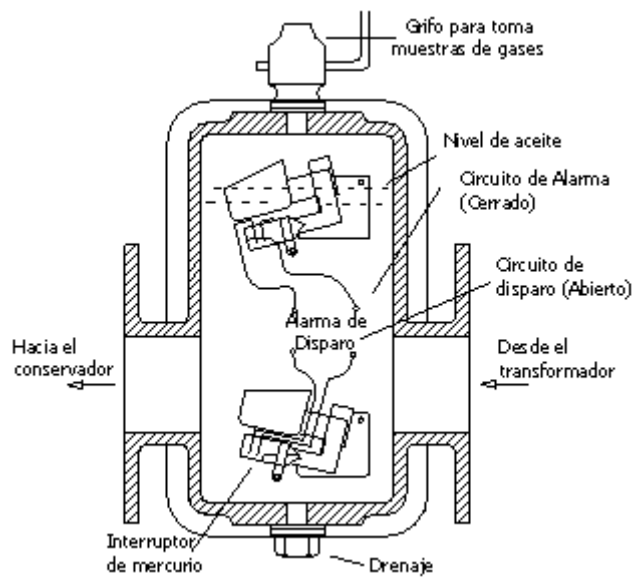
Detalles constructivos del relevador Buchholz.
